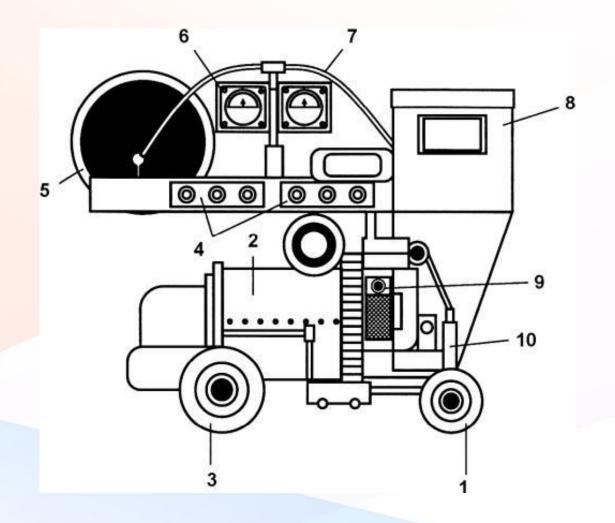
Сварочный трактор ТС-17М: 1 – направляющие колёса; 2 – электродвигатель для подачи электродной проволоки и передвижения трактора; 3 – ведущие колёса; 4 – пульт с кнопками управления; 5 – кассета с электродной проволокой; 6 – электроизмерительный прибор; 7 – электродная проволока; 8 – бункер для флюса; 9 – механизм подачи проволоки; 10 – мундштук.
